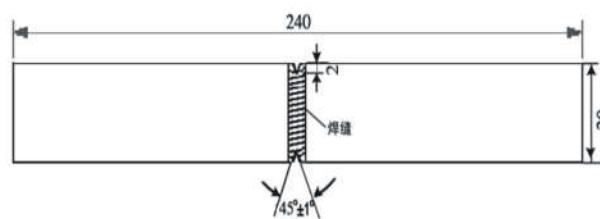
缺口焊缝拉伸试样的几何尺寸
